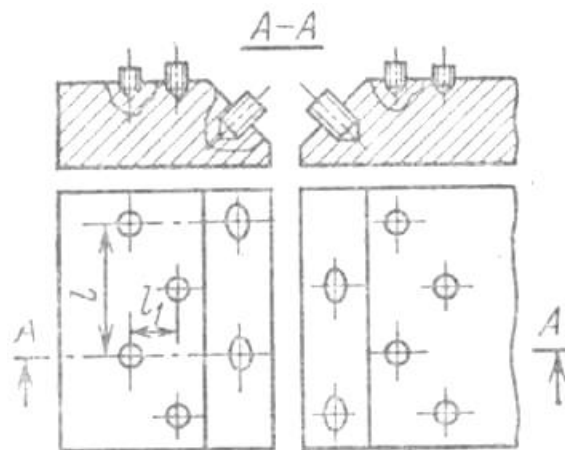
Підготовка чавунних деталей під зварювання за допомогою шпильок. l і l_1 - відстані між шпильками.
